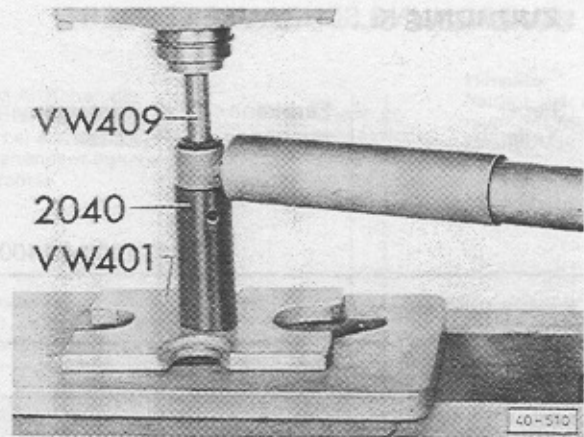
Gummilager und Buchse für Stoßdämpfer auspressen
